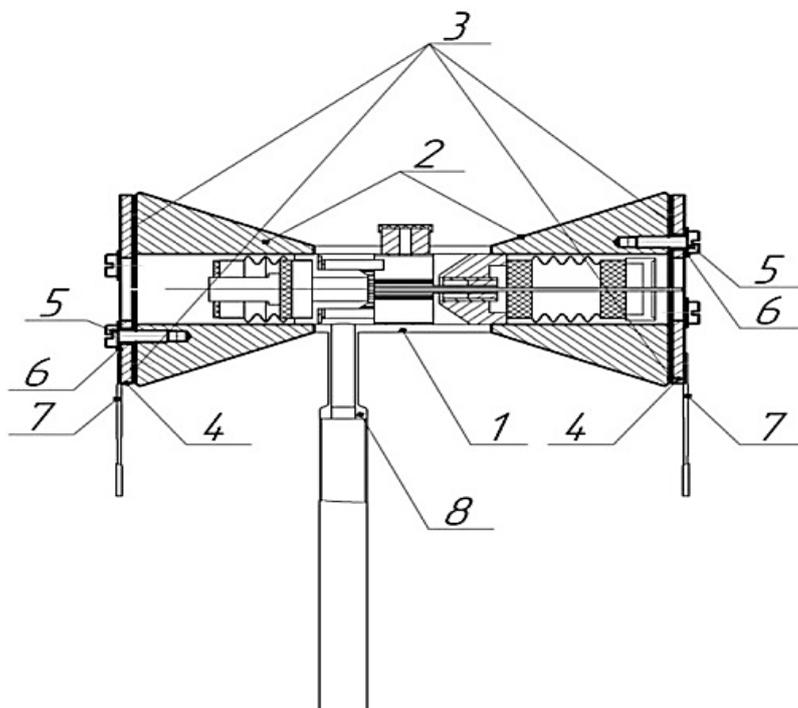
Сборочный чертеж магнетрона с прикрепленной УЗ оснасткой.
